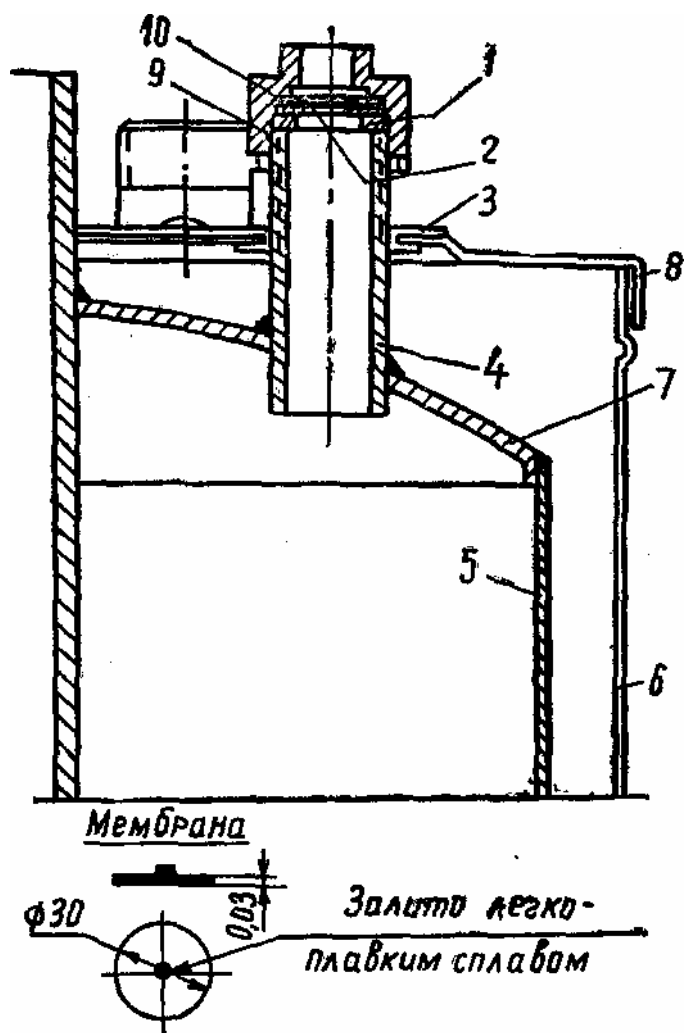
Схема предохранительного клапана: 1—промежуточное кольцо; 2—мембрана; 3—шайба; 4—труба; 5—бак; 6—кожух; 7—верхняя крышка; 8—крышка кожуха; 9—корпус; 10—прокладка.
